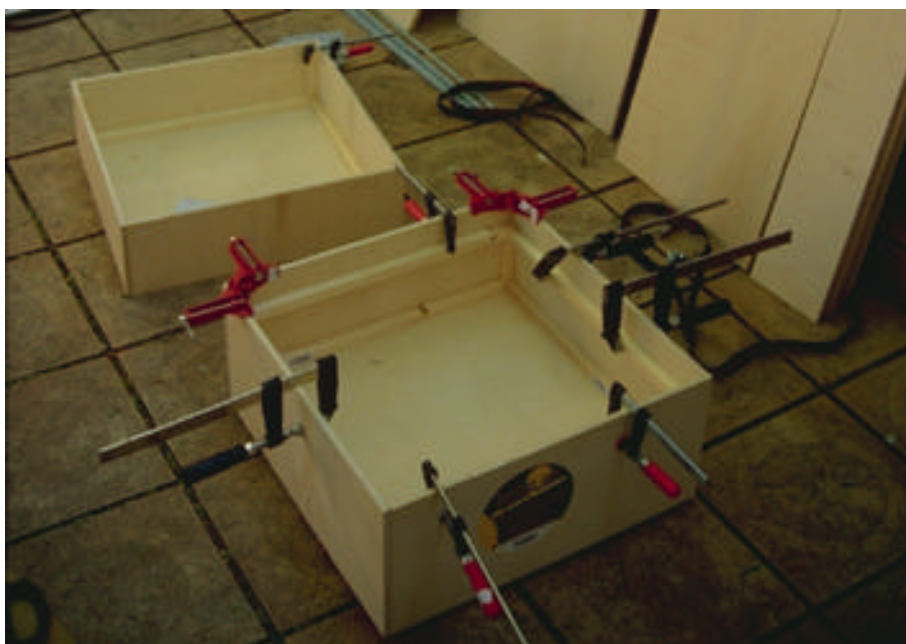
De eerste avond zit er op. Twee kisten van camerabatterijen in ruwbouw staan gereed. De houtlijm droogt.
